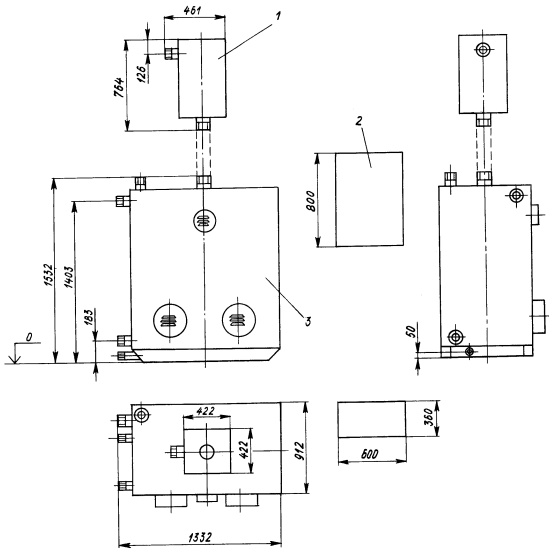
Габаритные размеры электроводонагревателя ЭВСАН-1000/15
